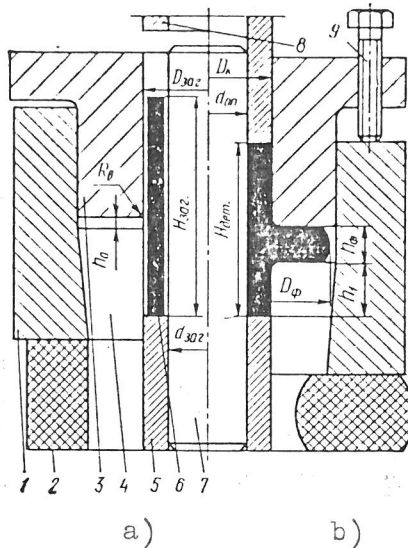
Werkzeug zum Fließpressen von Flanschteilen:
